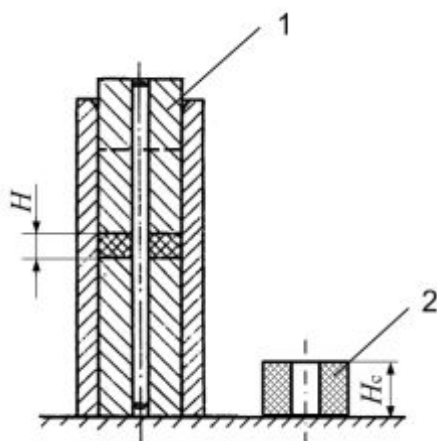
Процесс прессования втулочного УДЭ: 1 - прессовка; 2 - готовый УДЭ
